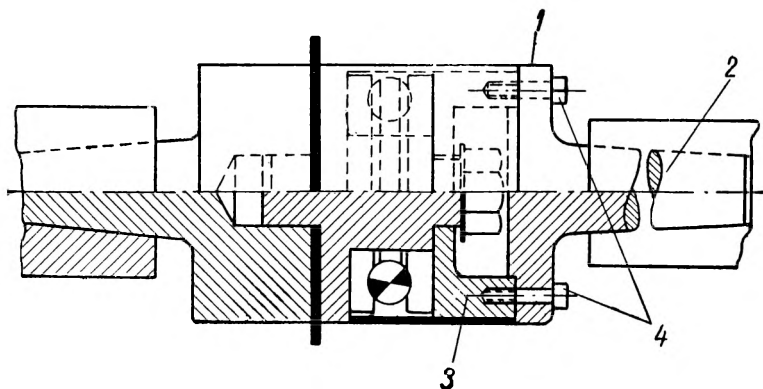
Приспособление для зажима тонких дисковых заготовок.
